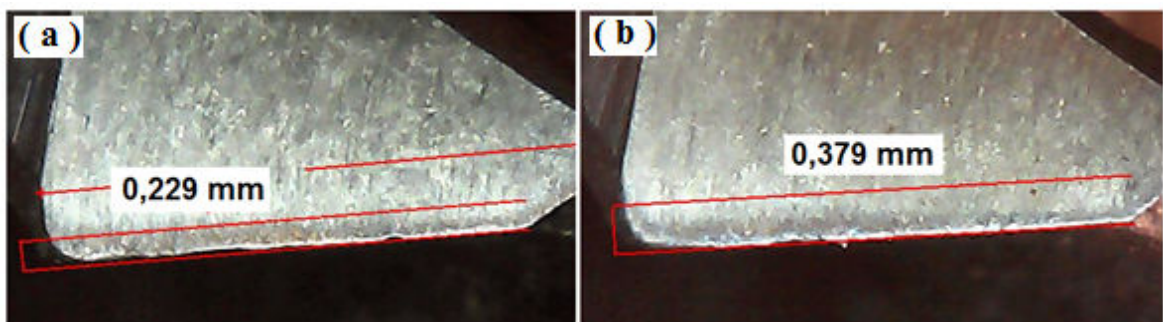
Desgaste de flanco das brocas com TiAlN desgastadas: (a) comprimento usinado de 3072 mm, (b) comprimento usinado de 4608 mm
